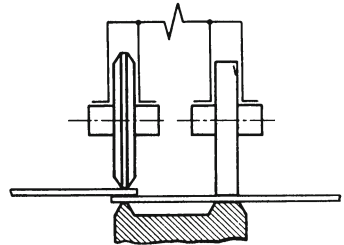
Schweißen einer Naht, Stromzuführung durch die zweite Rolle.
